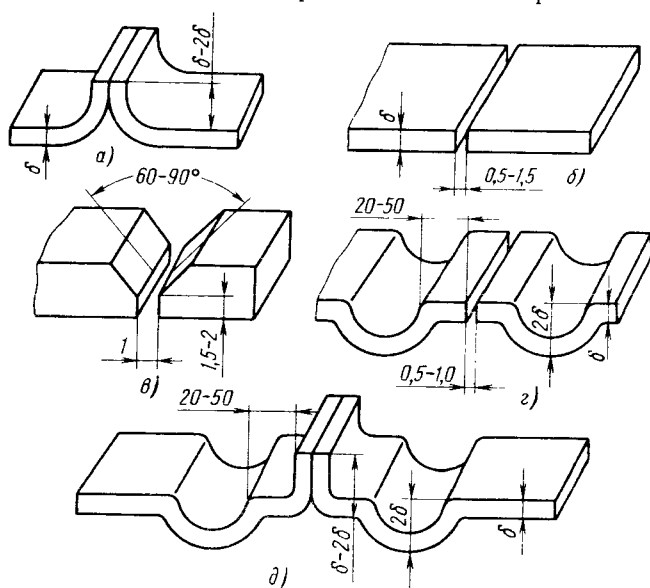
Подготовка кромок шва перед сваркой
